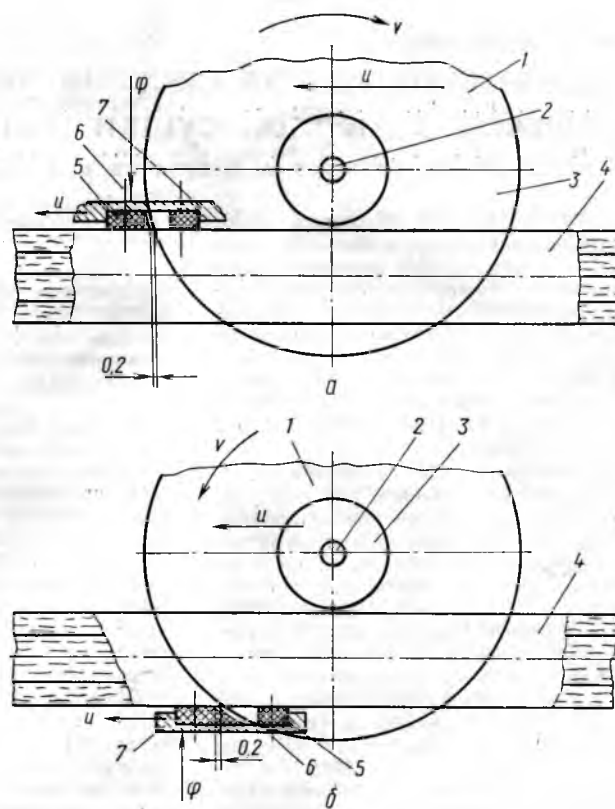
Схемы расположения узла искусственного подпора для круглопильных станков с верхним расположением пилы:
